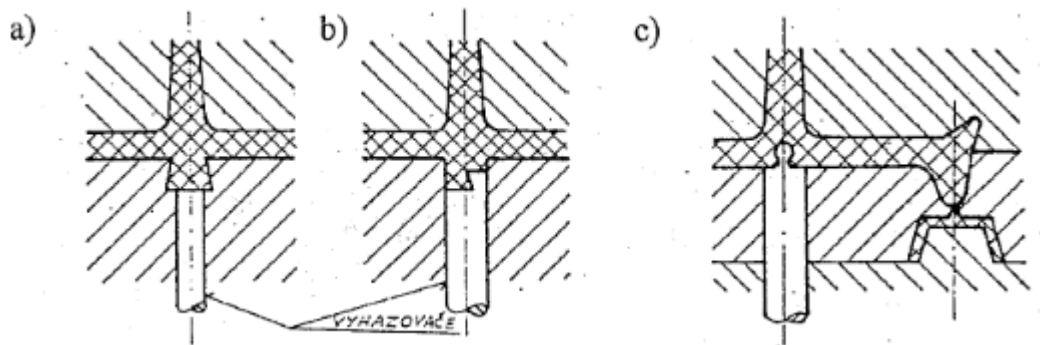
Tunelový vtok – oddělování při otevření formy [8]
